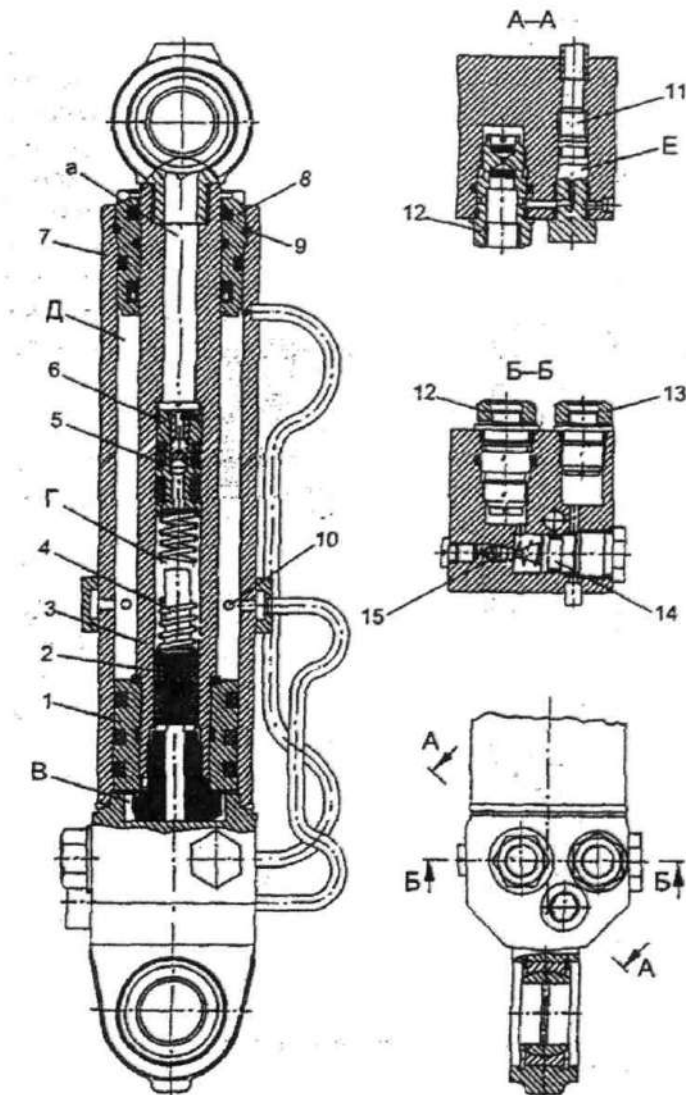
Гидроцилиндр механизма подъема кабины автомобиля
